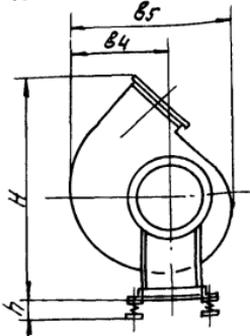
Вентиляторы В-Ц4-70-8; В-Ц4-70-10 с промежуточными диаметрами колес (исполнение 1). Габаритные и присоединительные размеры
